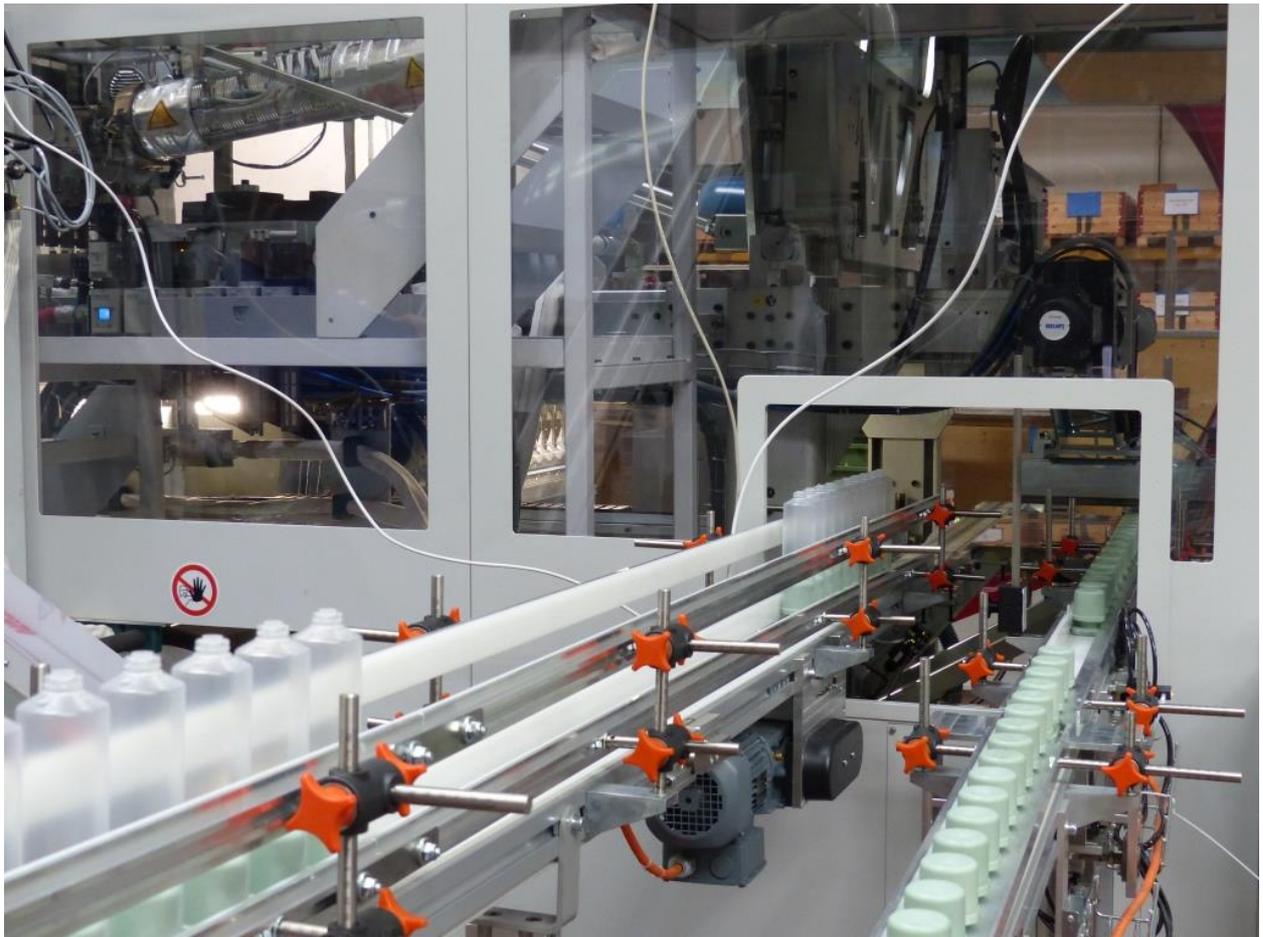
Transfer der Tuben aus der Maschine zum Verpackungsautomaten
